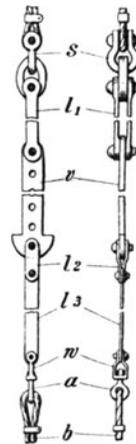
Unterseilgehänge mit Ausgleichvorrichtung für Seillängen.
